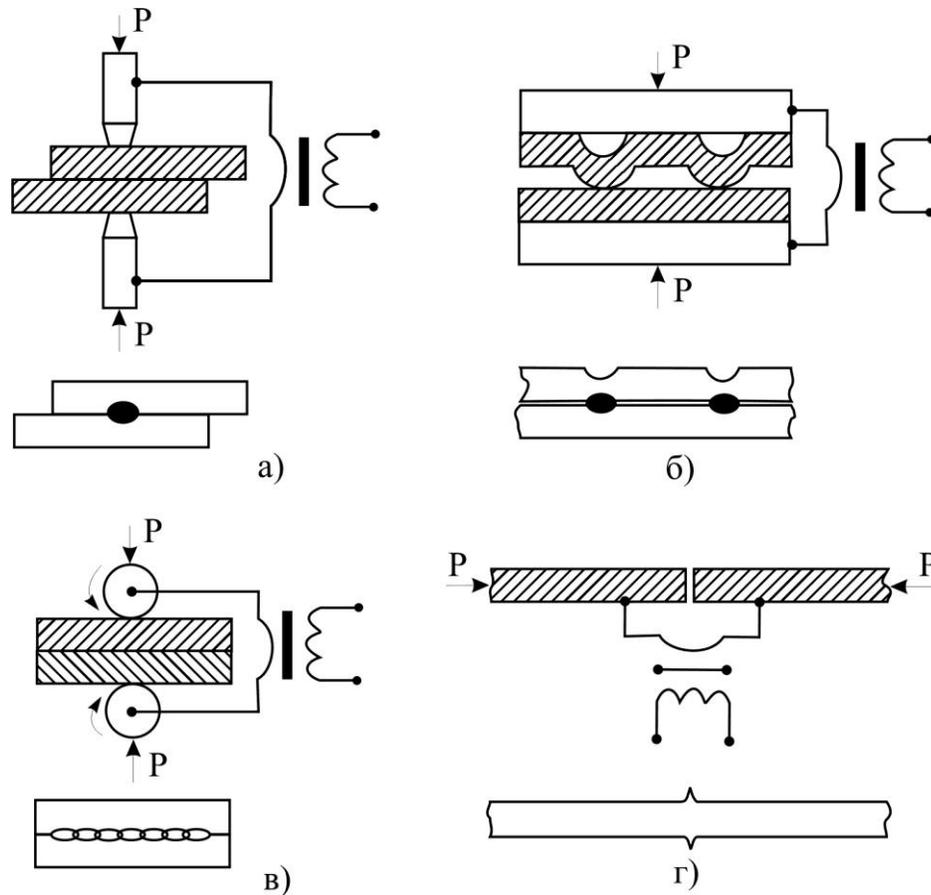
Схемы процессов и швов, условные обозначения видов контактной сварки: а – точечная (K_T); б – рельефная (K_B); в – шовная (K_P); г – стыковая (K_C).
